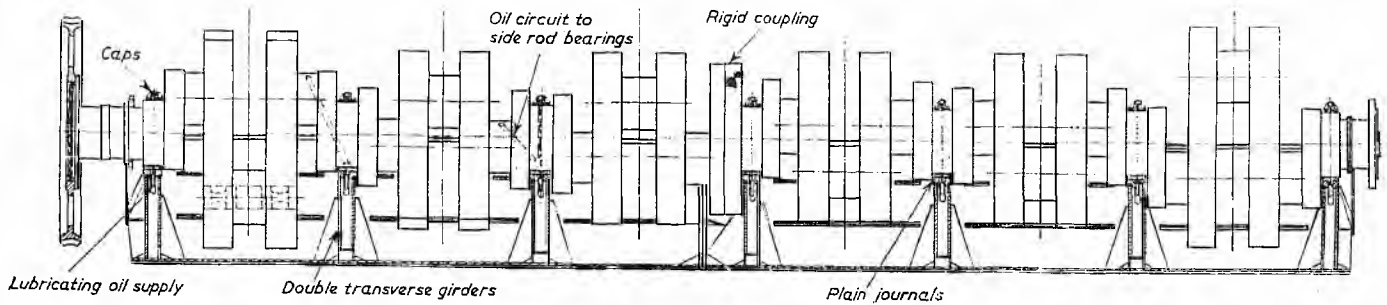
Fundatieplaat, hoofdaslagers en krukassamenstel
